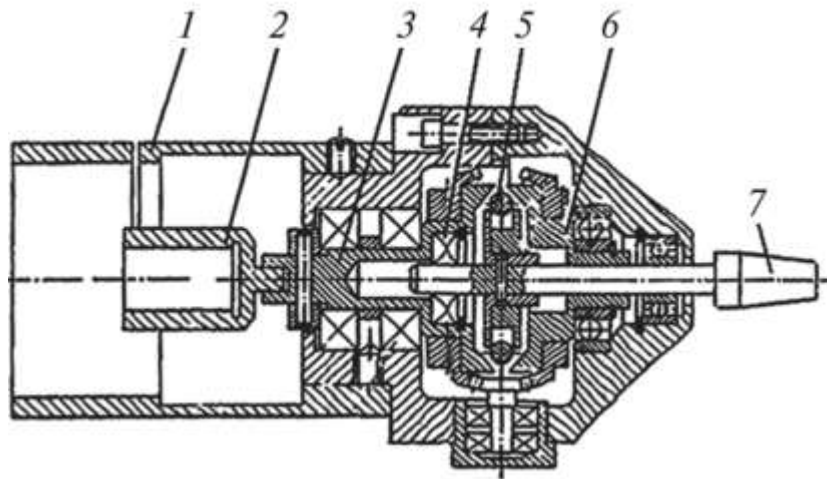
Конструкція реверсивного патрона для нарізування різьблення мідчиком
